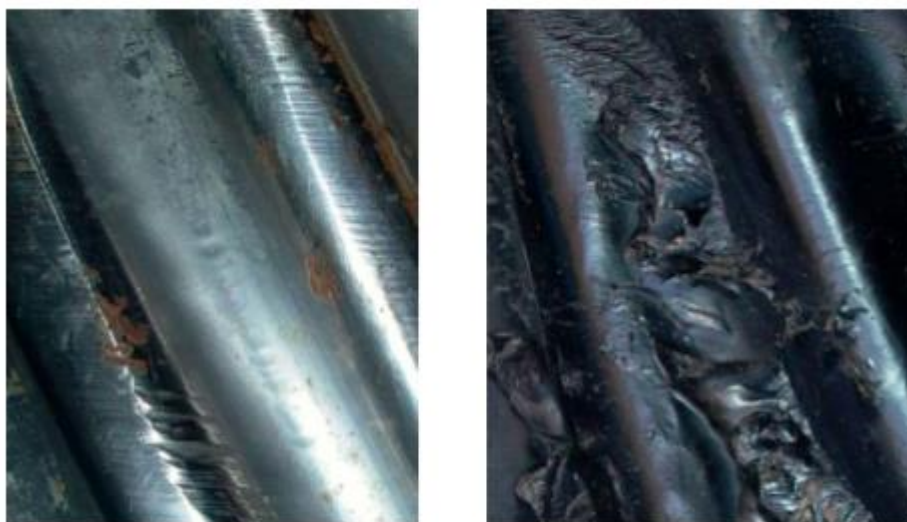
Износ поверхностей ротора и статора винтового забойного двигателя: а – износ поверхности ротора; б – износ поверхности статора
